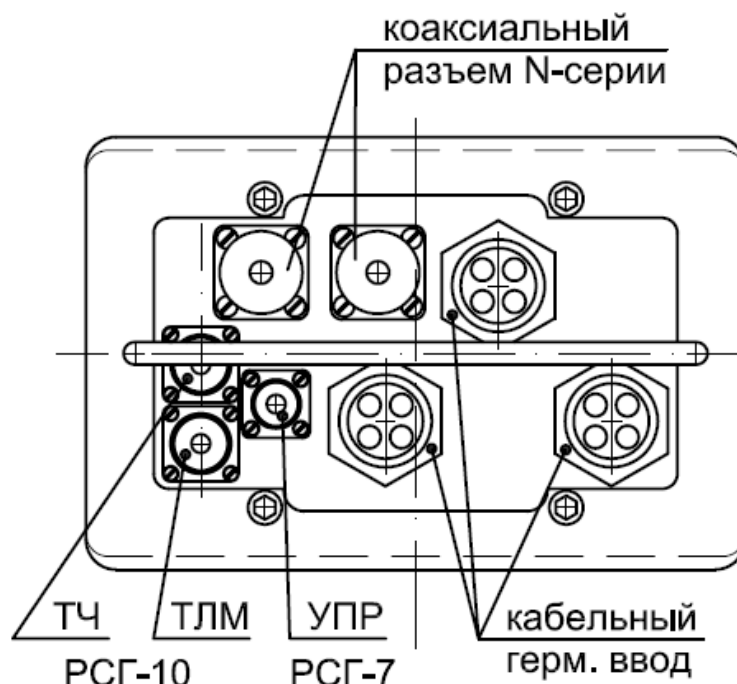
Корпус MGS-3-CASE-ST-BK300, вид сверху
